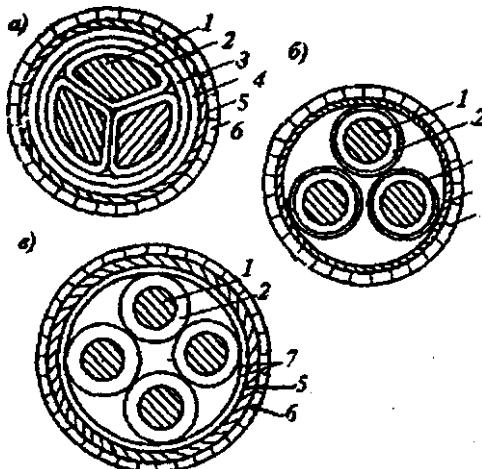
Конструкция кабелей 1 ...35 кВ: а - кабель на напряжение до 10 кВ с бумажной изоляцией; б - то же - с резиновой; в - то же на напряжение 20 и 35 кВ; 1 - токопроводящая жила; 2 - фазная изоляция; 3 - поясная изоляция; 4 - свинцовая или алюминиевая оболочка; 5 - броня; 6 - защитные покровы; 7 - обмотка лентой
